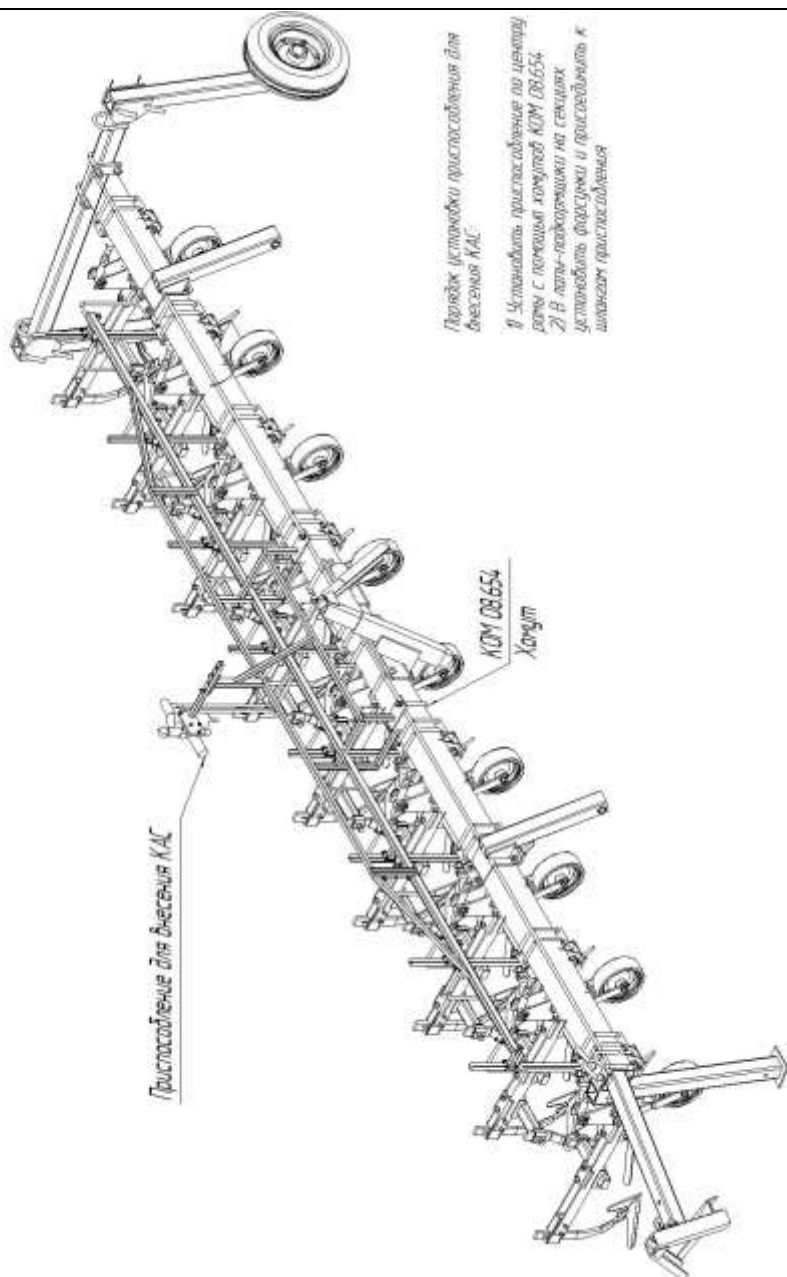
Установка рамки с регулятором и распылителями на культиватор
